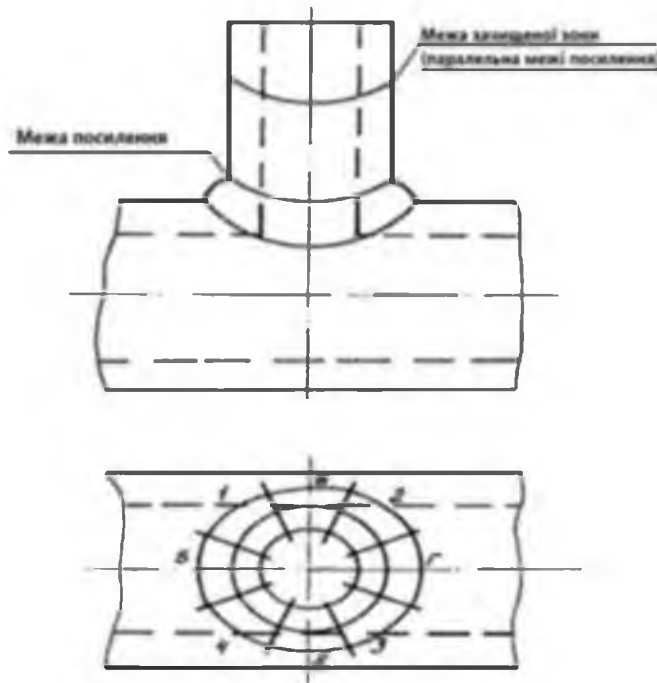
Схема розмітки кутового зварного з'єднання на сектори
